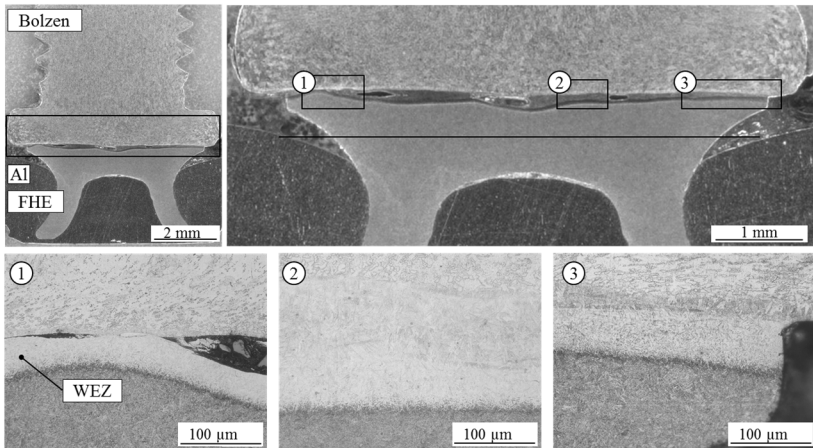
Repräsentativer Makroschliff einer Bolzen-Schweißung nach dem Primärprozess
